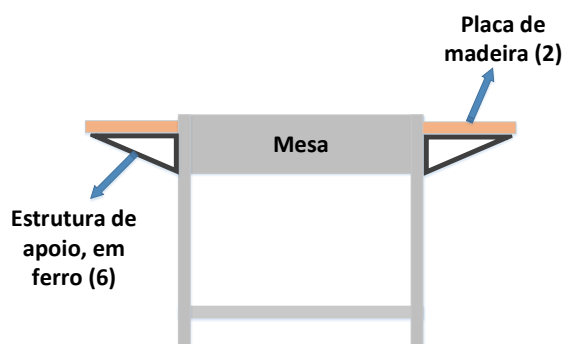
Corte transversal da mesa com as placas de madeira, fixas através das estruturas em ferro.
